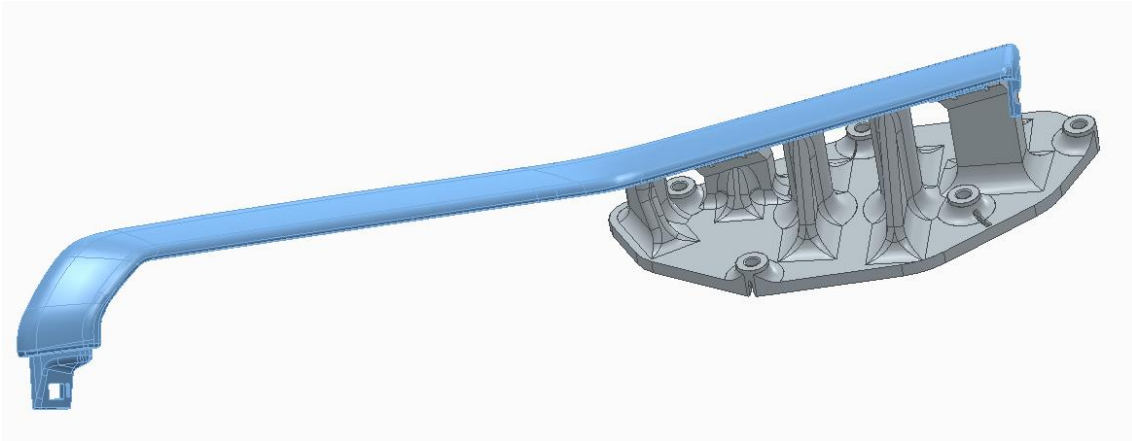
Módulo 1 del utillaje 2 con pieza de trabajo incorporada
